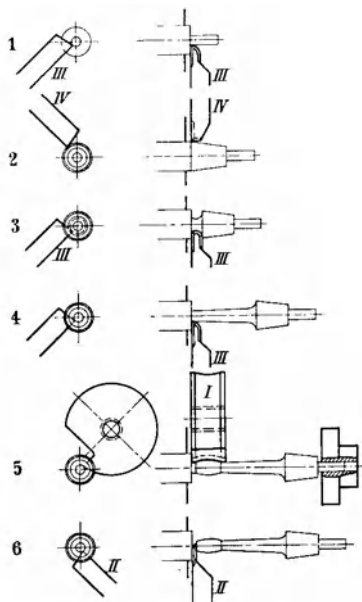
Bearbeitung eines Hahnkegels aus Messing.
